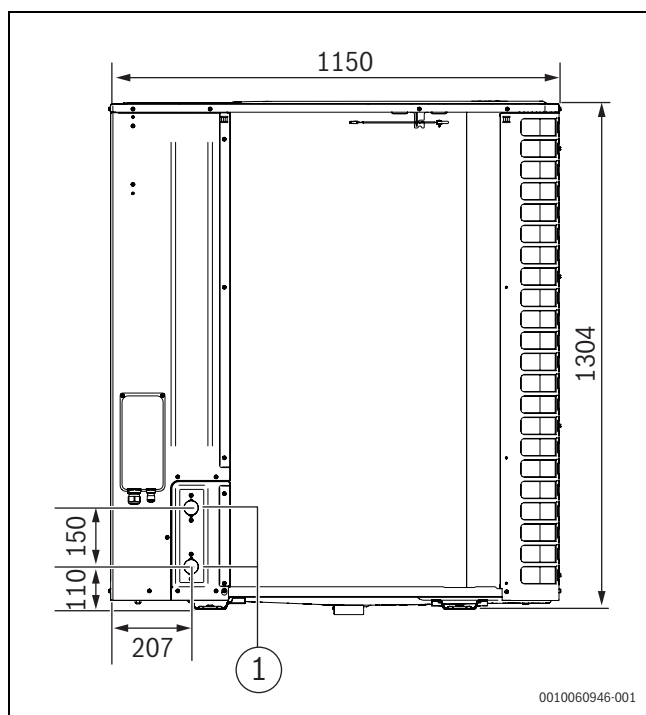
Dimensions et raccords hydrauliques de la pompe à chaleur, vue arrière
